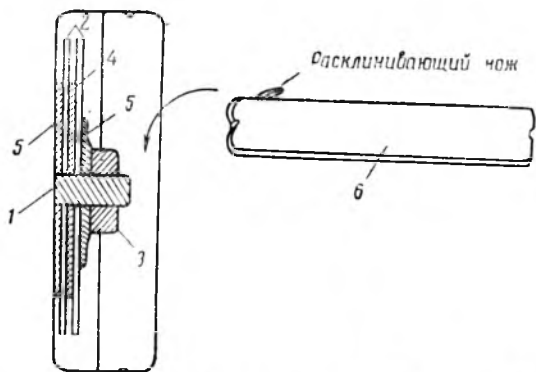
Схема переоборудованного станка ЦА-2: 1 — вал пильных дисков; 2 — пильные диски; 3 — гайка для зажима дисков на пильном валу; 4 — прокладка между дисками; 5 — фланцы; 6 — металлическая доска с расклинивающим ножом, прикрывающая окно для монтажа пильных дисков на валу вровень с поверхностью стола станка
